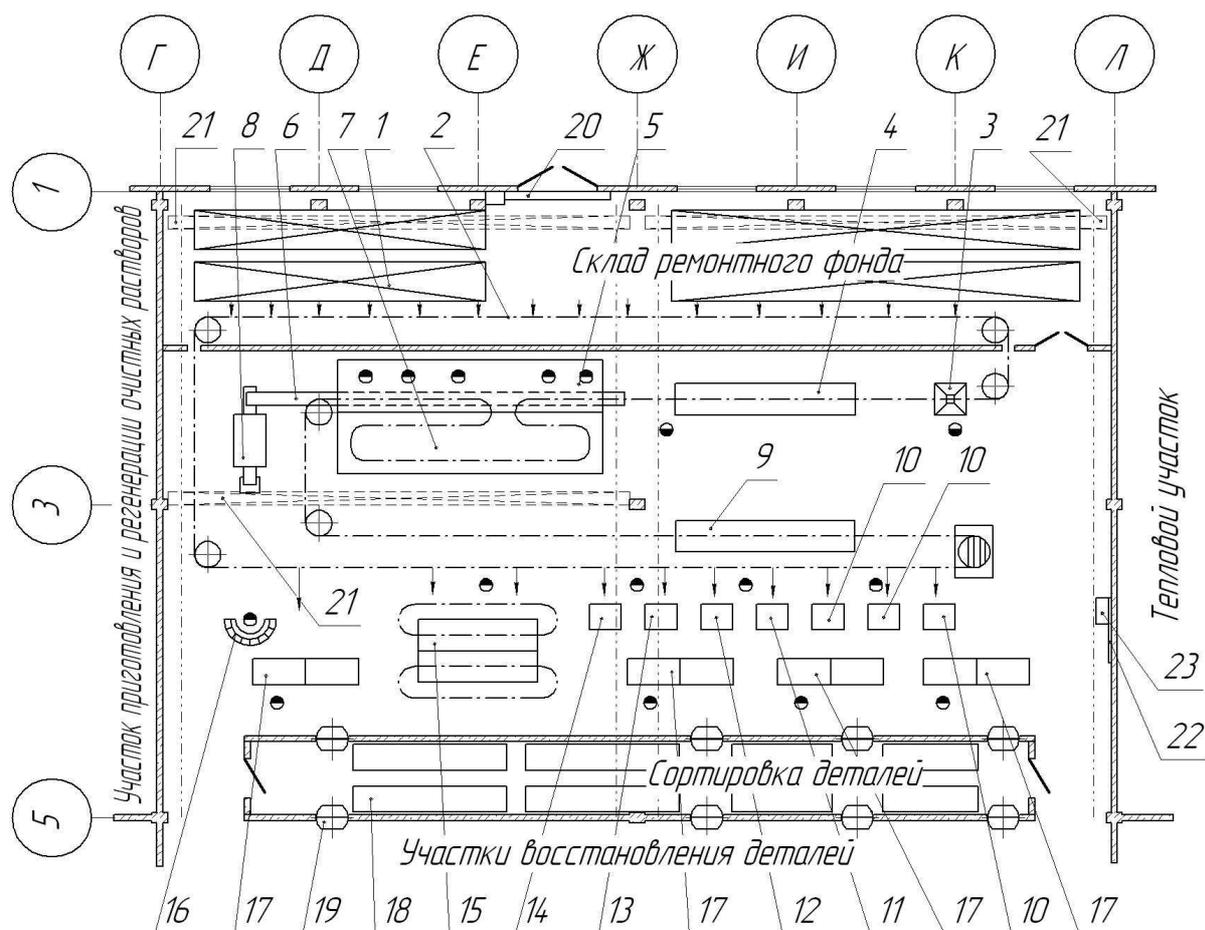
Планировка участка разборки двигателей, очистки и сортировки деталей: 1 – подставка под двигатели; 2 – подвесной конвейер; 3 – емкость для масла; 4 – струйная машина для наружной очистки; 5 – эстакада; 6 – ленточный транспортер для метизов; 7, 9 – погружные очистные машины; 8 – барабанно-шнековая машина для очистки метизов; 10 – погружная машина для очистки деталей; 11 – машина для очистки деталей косточковой крошкой; 12 – машина для очистки деталей стеклянными шариками; 13 – машина для очистки деталей от накипи; 14 – машина для очистки масляных каналов; 15 – машина для очистки деталей в расплаве солей и щелочей; 16 – стенд для сортировки метизов; 17 – стенд для определения трещин и сортировки деталей; 18 – стеллаж для деталей; 19 – поворотный стеллаж; 20 – тепловая завеса; 21 – кран-балка ( $q = 2 \text{ тс}$ ); 22 – противопожарный щит; 23 – ящик с песком
